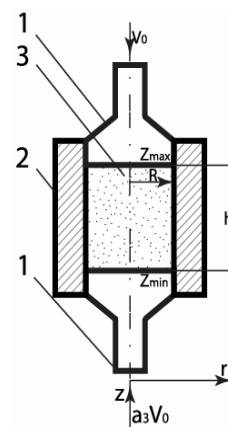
Принципиальная схема двустороннего закрытого прессования: 1 – пуансон; 2 – пресс-форма; 3 – заготовка (композиционный материал)
